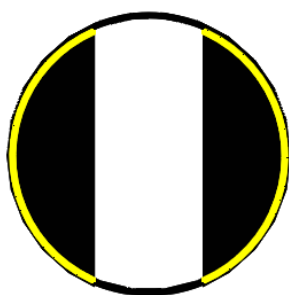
Cordones de soldadura (Fuente: propia)
